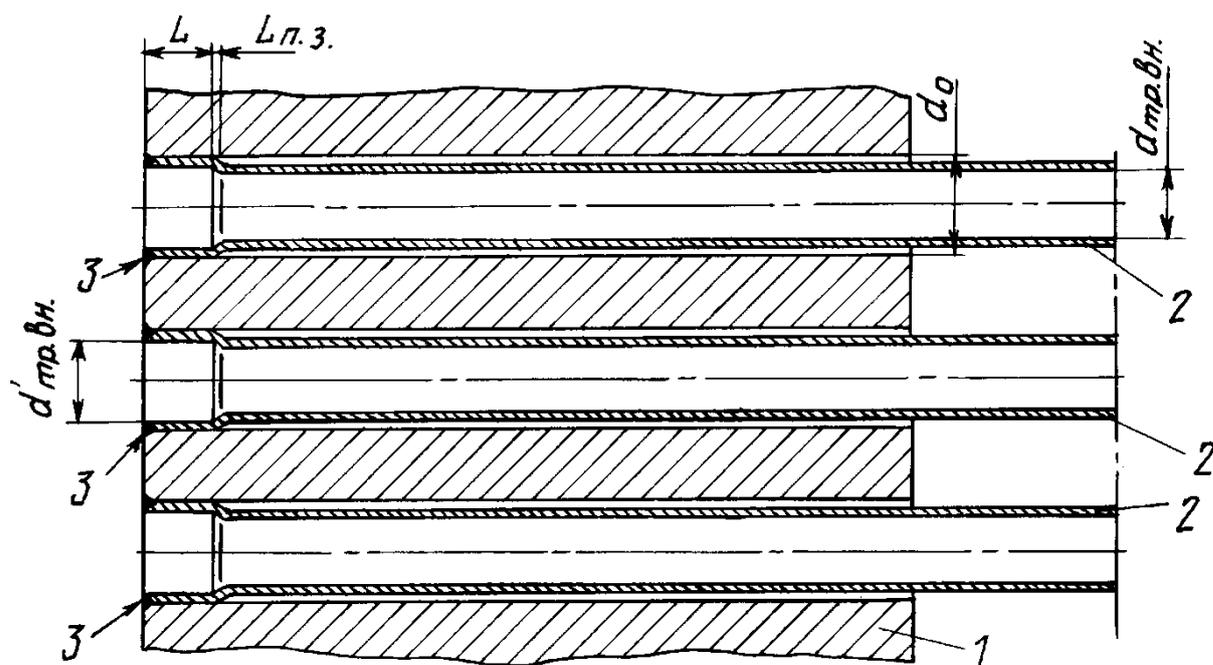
Комбинированный способ сварки труб с трубной доской
